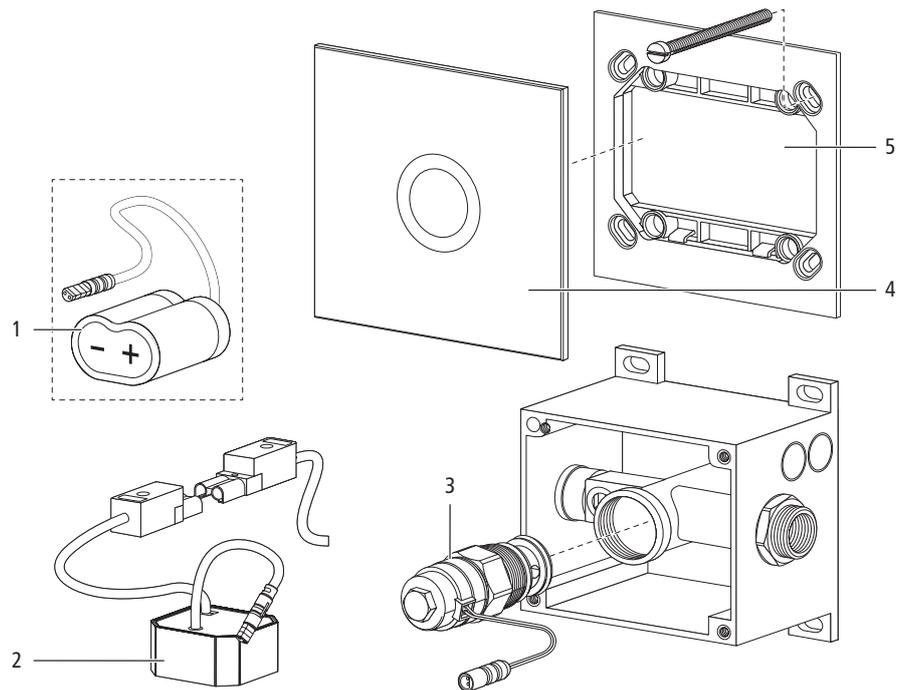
Pièces de rechange commande infrarouge More 1 (71009)
